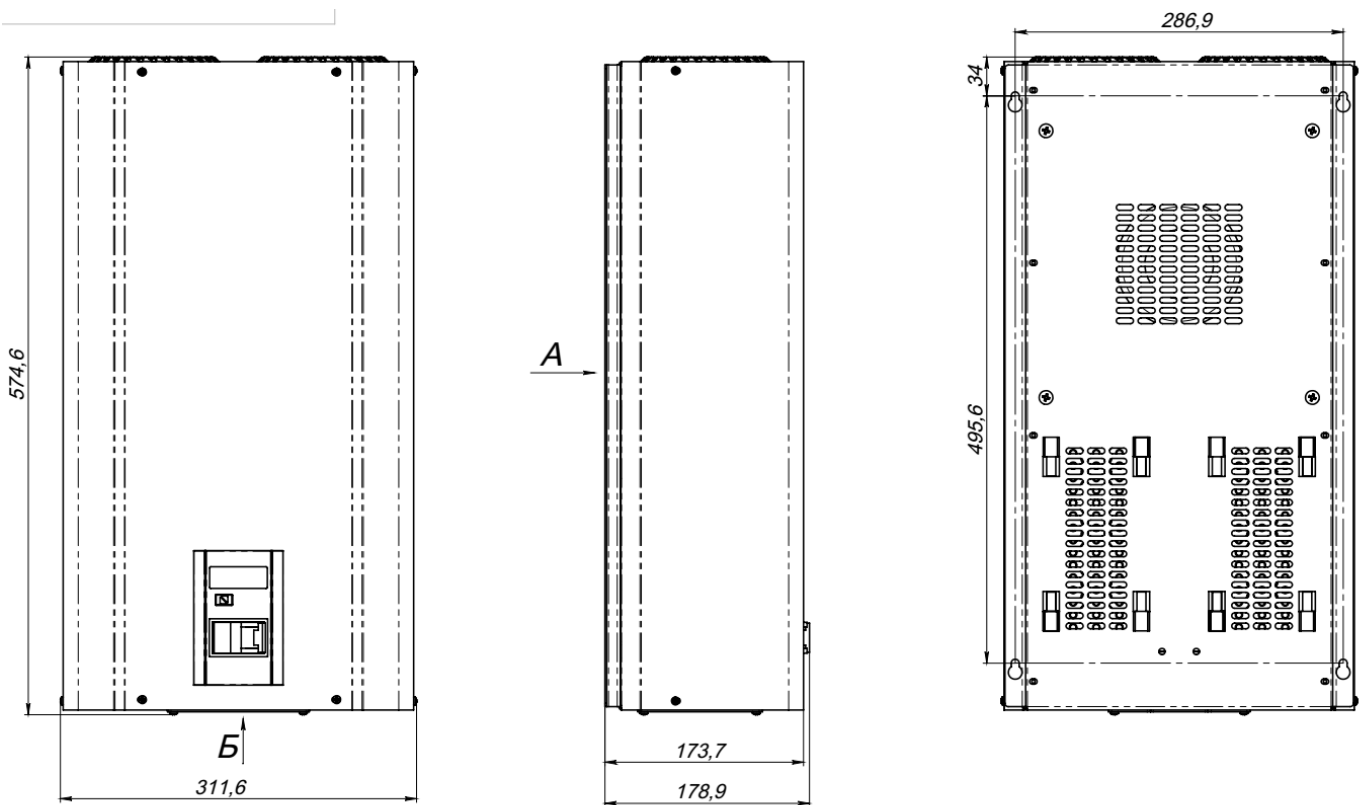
Габаритные и установочные размеры стабилизаторов ГИБРИД на 80А
